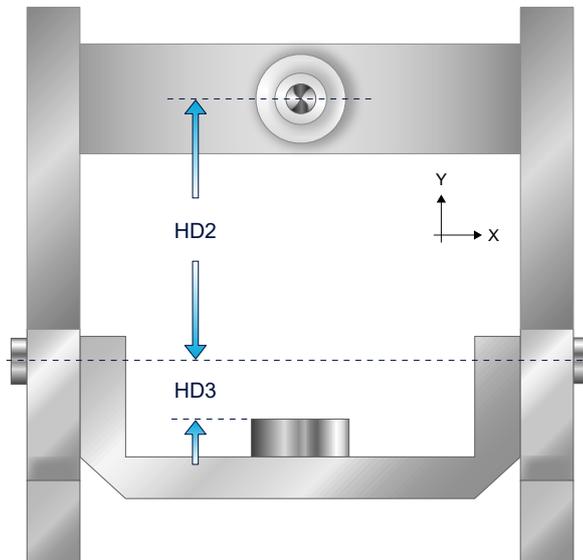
Kinematik der 5-achsigen Fräsmaschine
